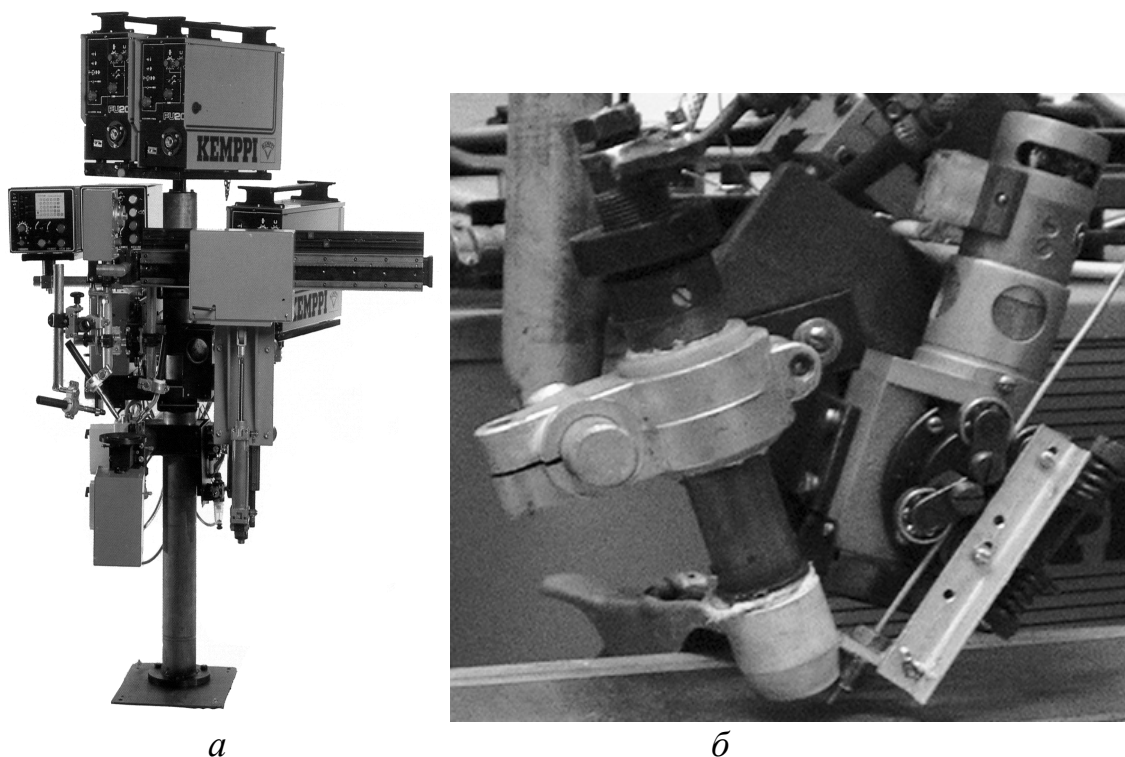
Установка КМ-50 (а) и сварочная головка (б) для процесса дуговой наплавки антифрикционных покрытий
